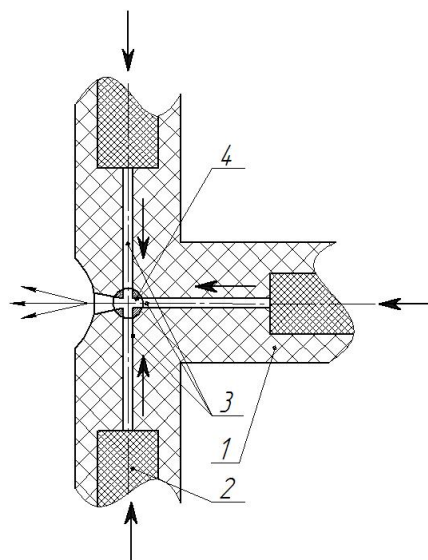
Устройство ЭП с увеличенной энергией импульса: 1 – корпус из электроизоляционного материала, например, из нитрида бора; 2 – импульсный гидравлический затвор; 3 – капиллярный канал, выполненный в корпусе и соединяющий гидравлическое сопротивление 2 с выходом из корпуса 1; 4 – электрод, установленный в корпусе 1 на выходящем наружу конце капиллярного канала.
